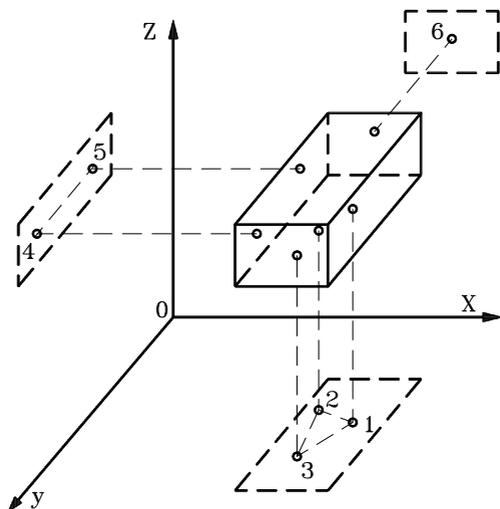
Схема полного базирования призматической заготовки (правило шести точек)
